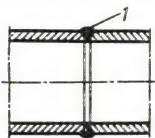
Сварное соединение: 1 — сварной шов.
